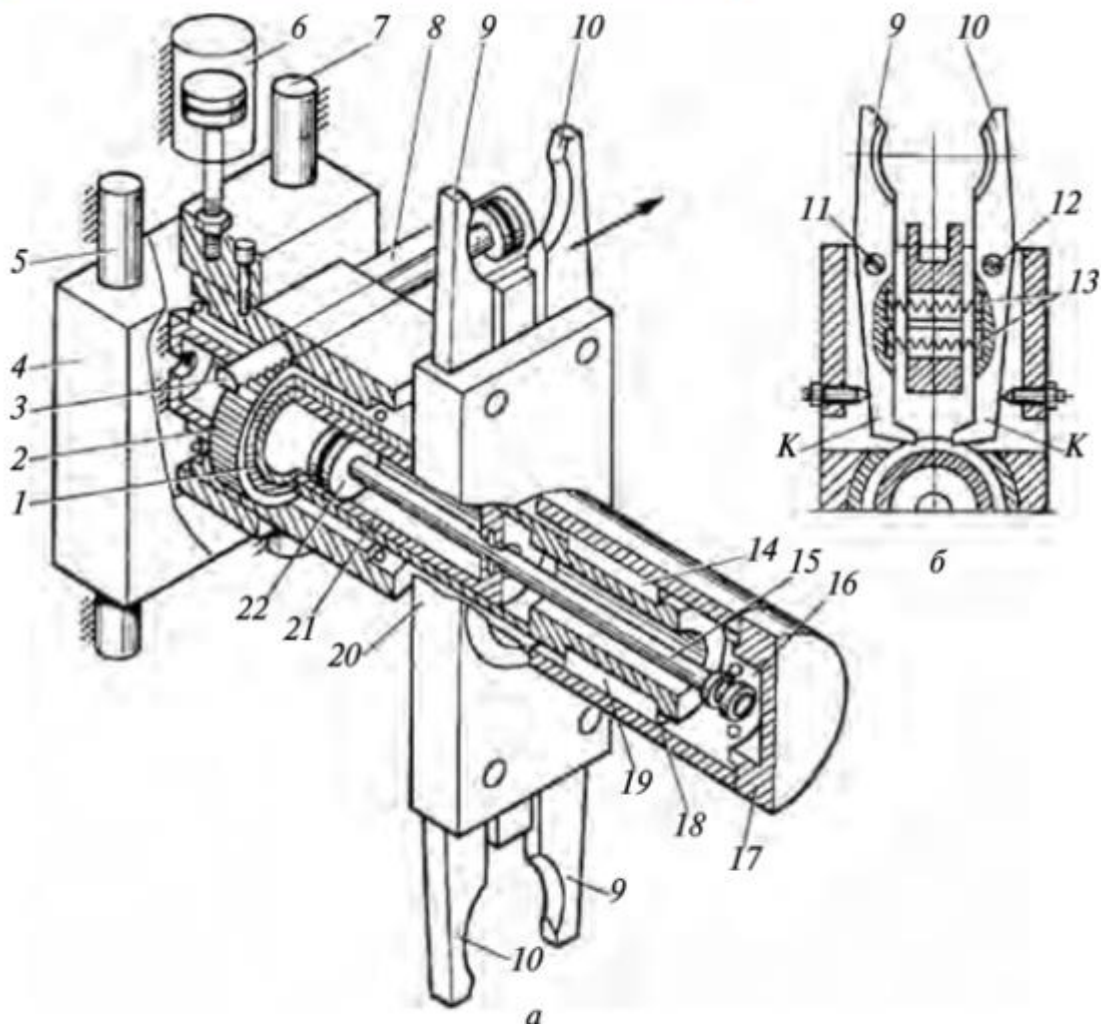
Автооператор, размещенный над шпиндельной бабкой многоцелевого станка (МС) модели ИР500МФ4: а — общий вид; б — захватное устройство; 1 — стакан; 2 — зубчатый венец;
